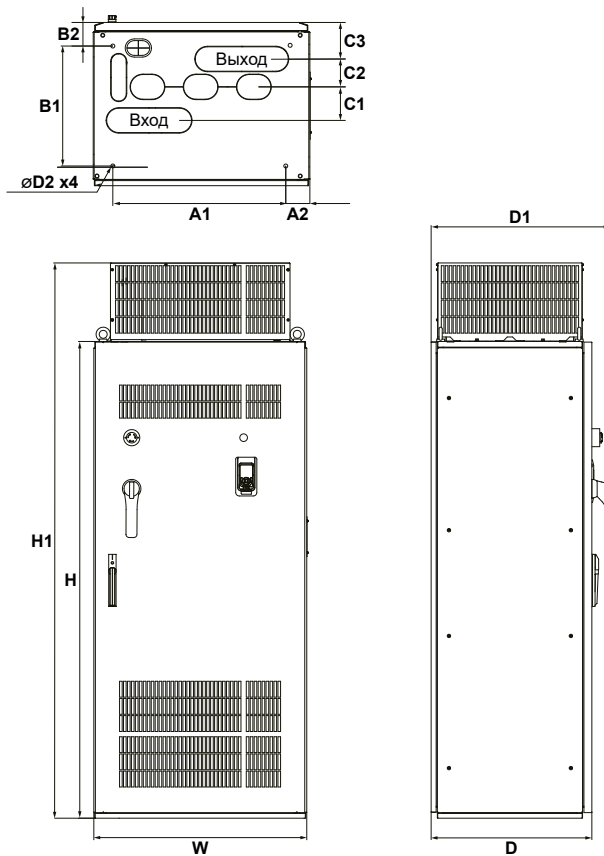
Внешний вид типоразмера Т13 (без распределительного щита)
